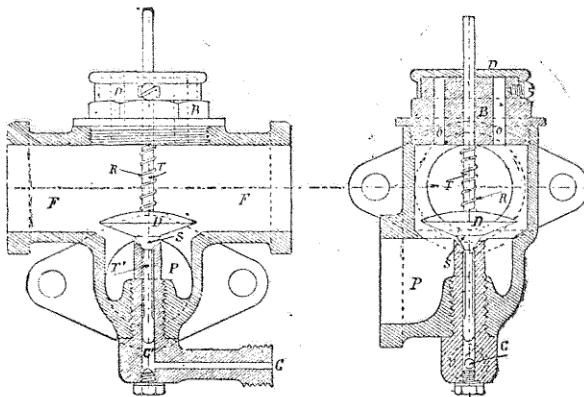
et 86. — Carburateur Gautier-Wehrle.
